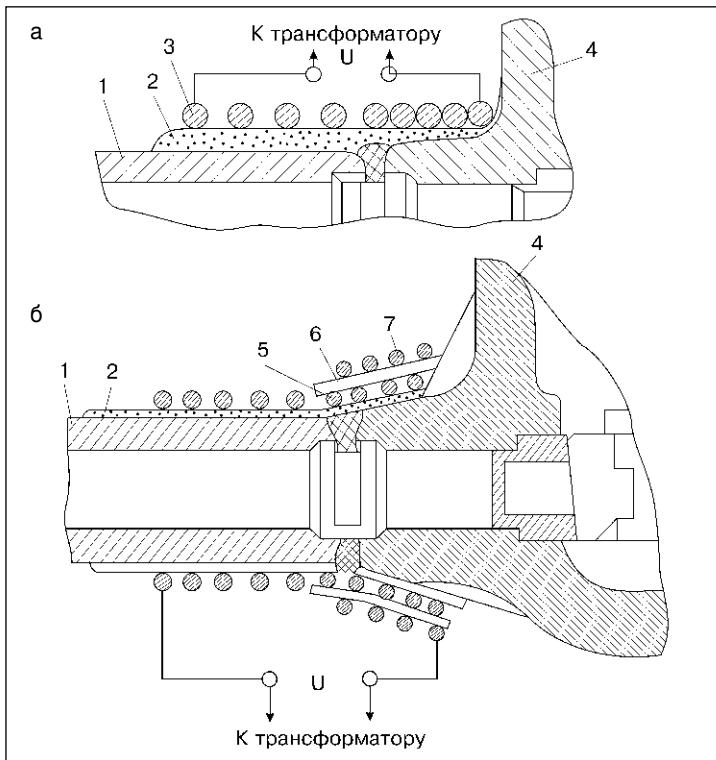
Схемы установки электронагревателей при термообработке сварных соединений труб с задвижками: а — с установкой индукторов или КЭН; б — с установкой двухслойного индуктора (1 — труба; 2 — теплоизоляция; 3 — индуктор или КЭН; 4 — задвижка; 5 — асбосцементная прокладка; 6 — внутренний слой индуктора; 7 — наружный слой индуктора)
